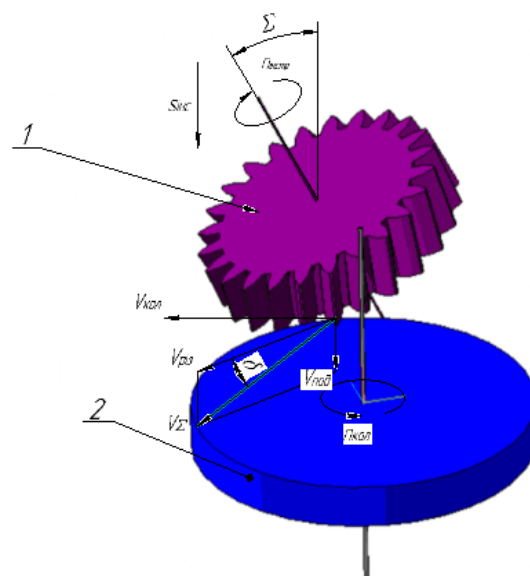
Кінематична схема розташування інструмент-заготовка при методі Power skiving
